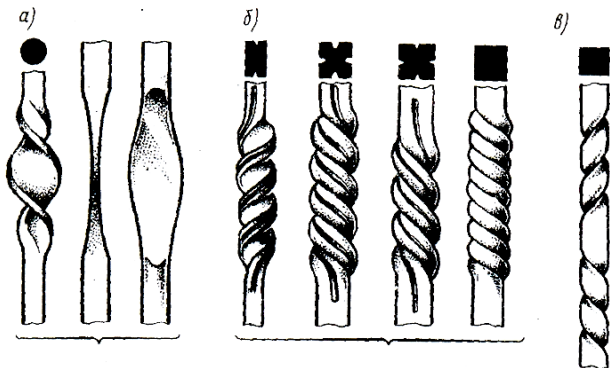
Скрутка стержней: а - предварительно раскованного круглого прутка; б - прямоугольных и квадратных прутков с бороздкой; в - двусторонняя скрутка квадратного прутка
